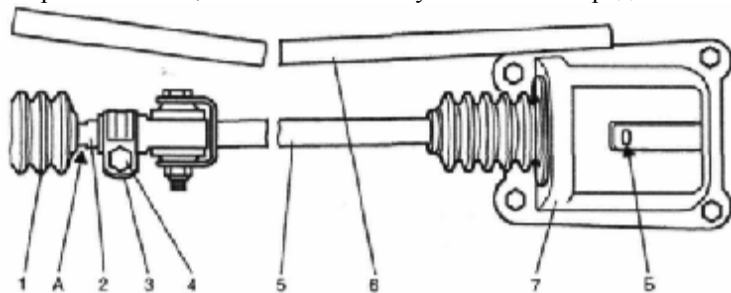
Регулировка привода управления коробкой передач (вид снизу):
